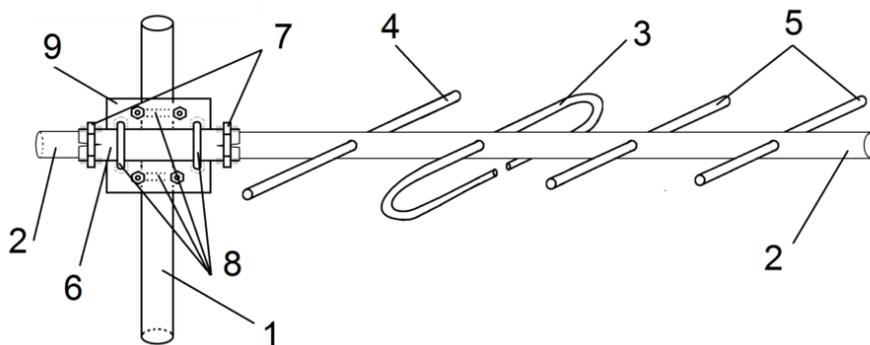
Чертеж радиоудлиннителя сотовой связи для мест неуверенного приема
